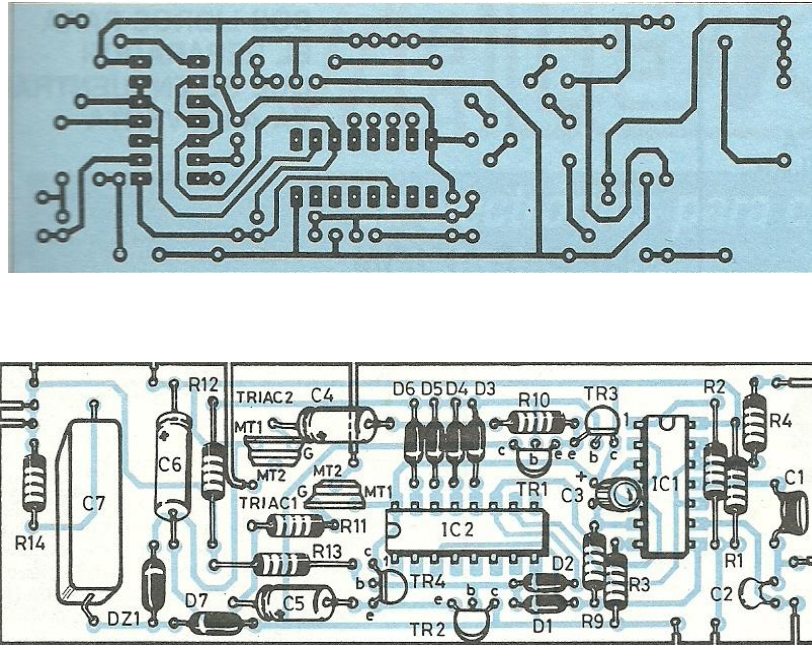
Dibujo de la placa de circuito impreso, a tamaño natural, por el lado de las pistas de cobres y por el lado de componentes.
